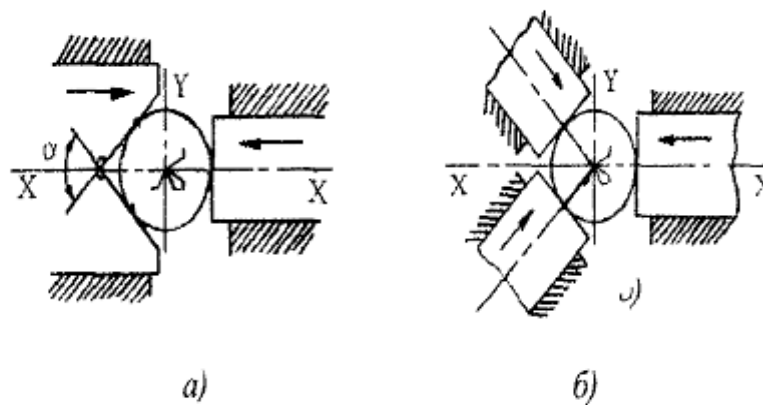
Двоступеневе центрування заготовки при використанні призм двома повзунами
